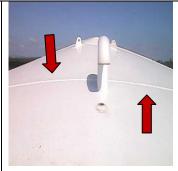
Tanque de Fuel Oil. Observe el cordón de soldadura.
